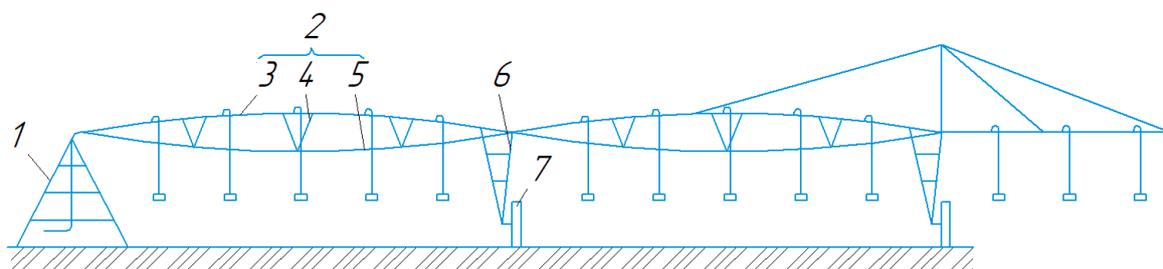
Схема дождевальной машины ферменной конструкции
